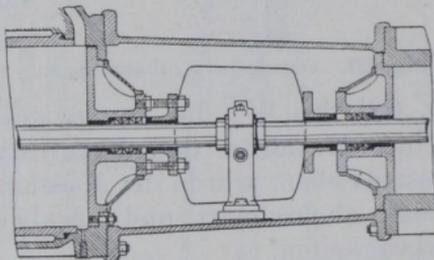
Lagerung der Kolbenstange zwischen den beiden Cylindern.
